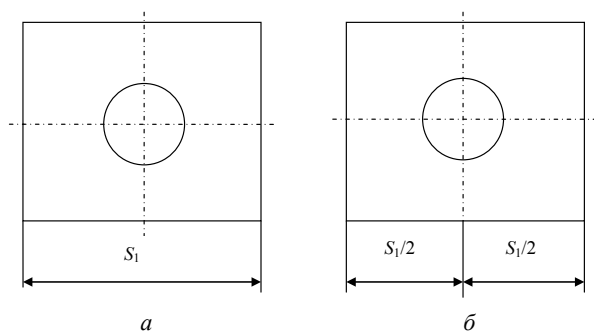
a* – размеры на чертеже детали; *б* – размеры на схеме обработки
